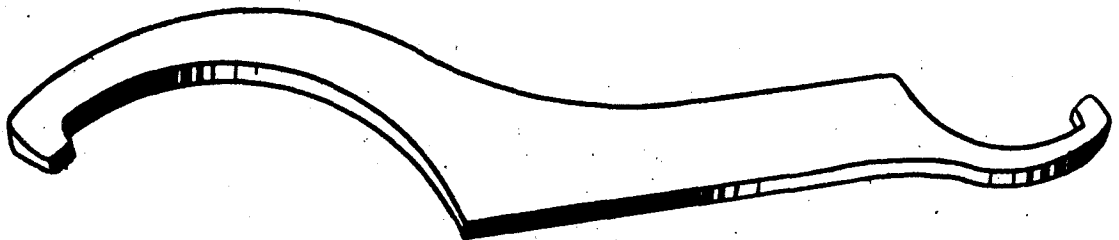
Специальный ключ для отвертывания гайки крепления подшипника промежуточной опоры
